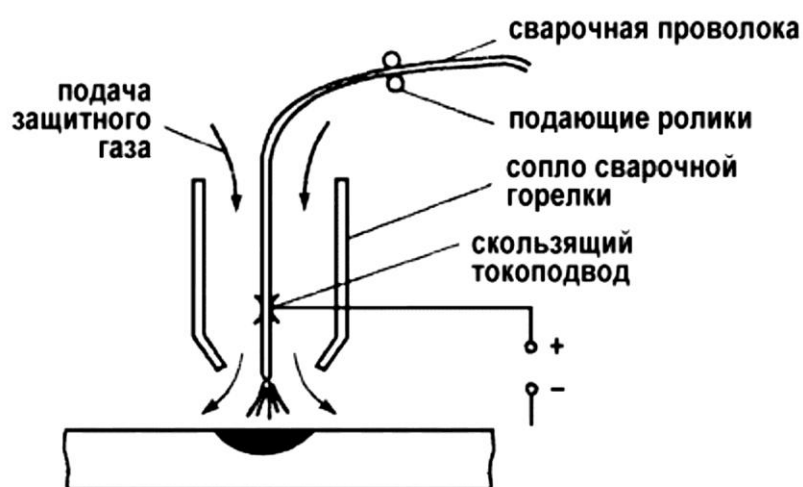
Сварка плавящимся электродом под защитой газа
